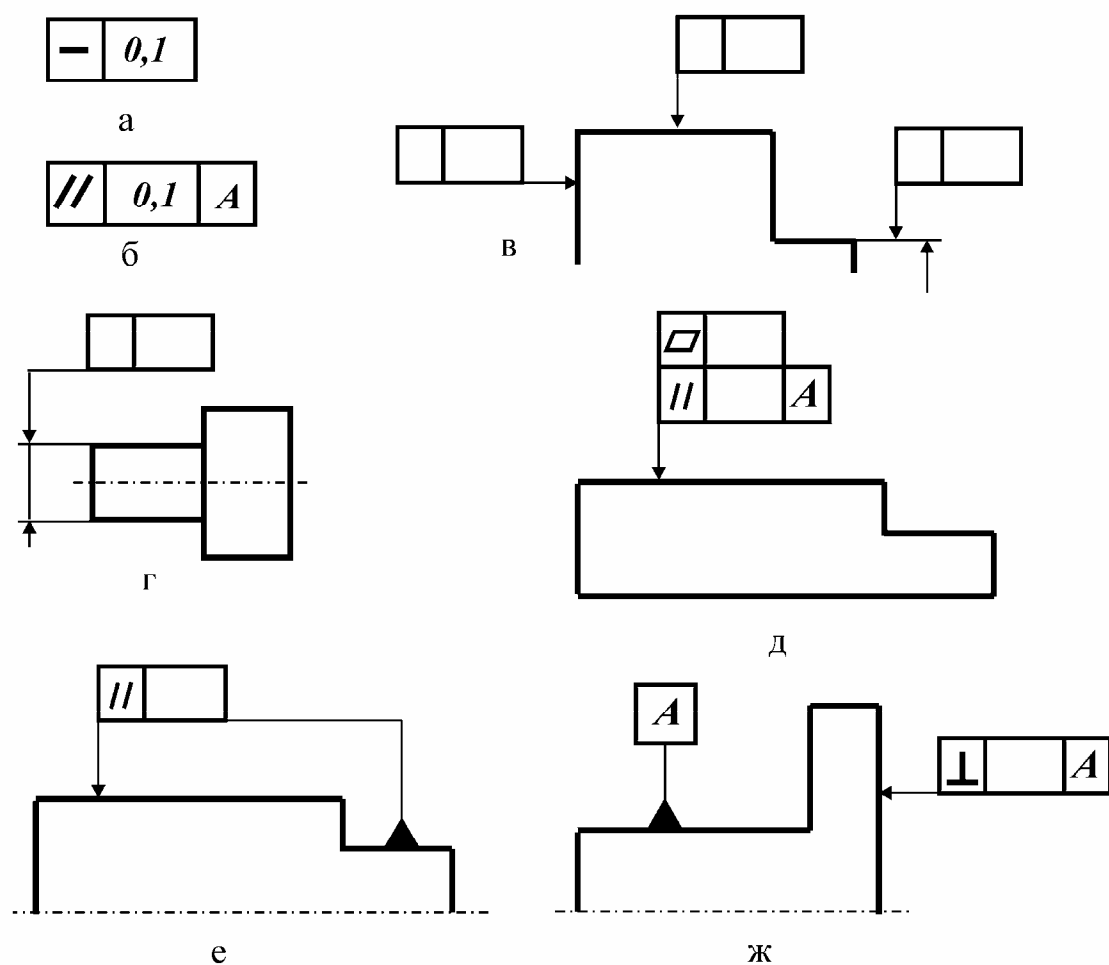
Обозначения на чертежах допусков формы и расположения поверхностей
